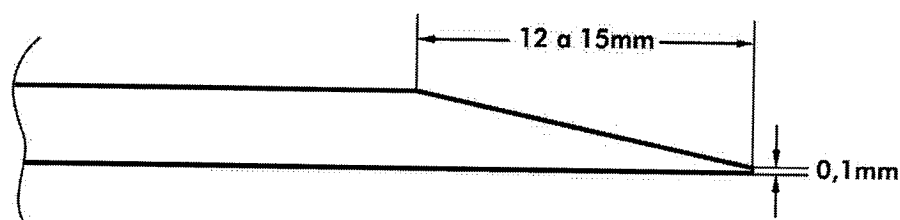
Dimensões do chanfro desquinado terminando em zero
